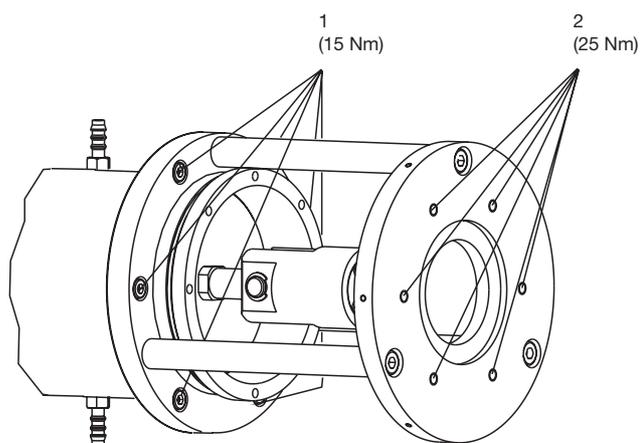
Module de dosage à piston (TZKa) Makro TZ
